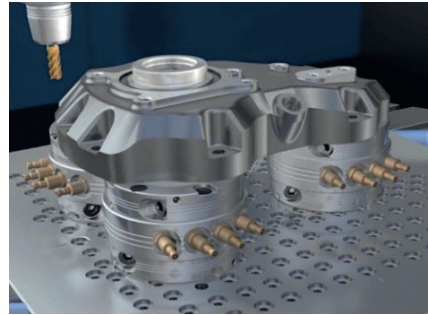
Установка деталей без зажимных приспособлений с доступом с пяти сторон
